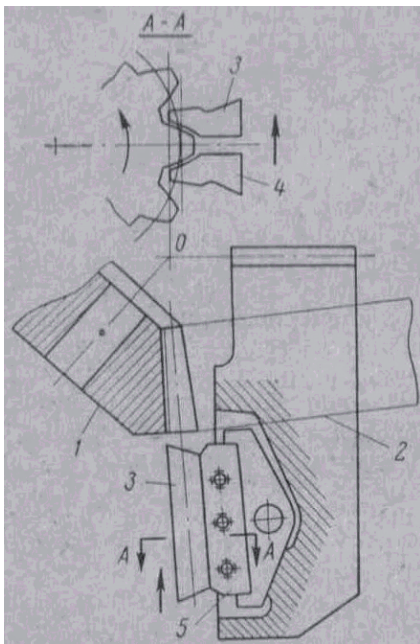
Нарезание зубьев конического колеса на зубошарофовальном станке: 1 – нарезаемое колесо; 2 – воображаемое колесо, зубья которого создаются двумя шарофовальными резцами; 3 и 4 – шарофовальные резцы
